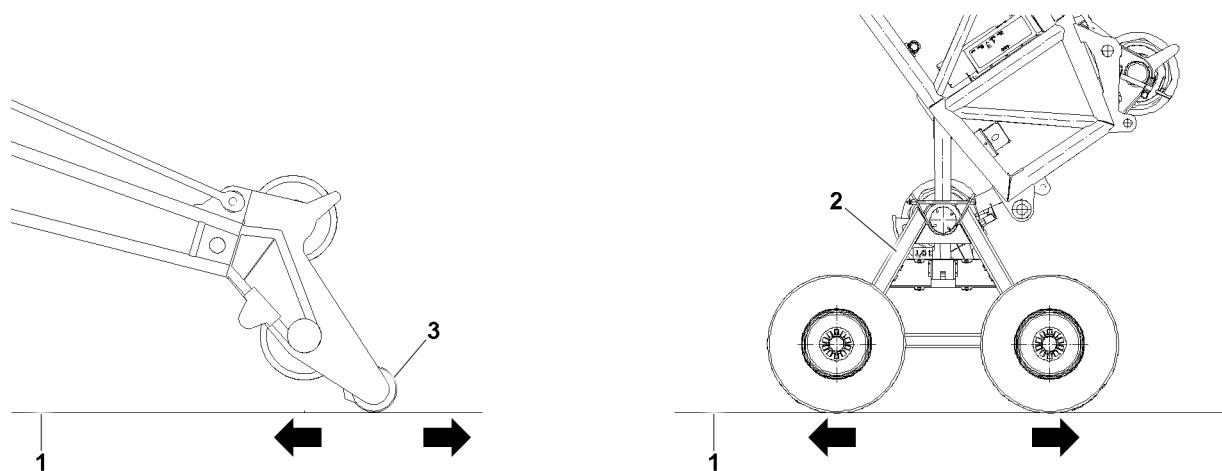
Calzada del carro de poleas o rodillo de rodadura del cabezal de celosía
